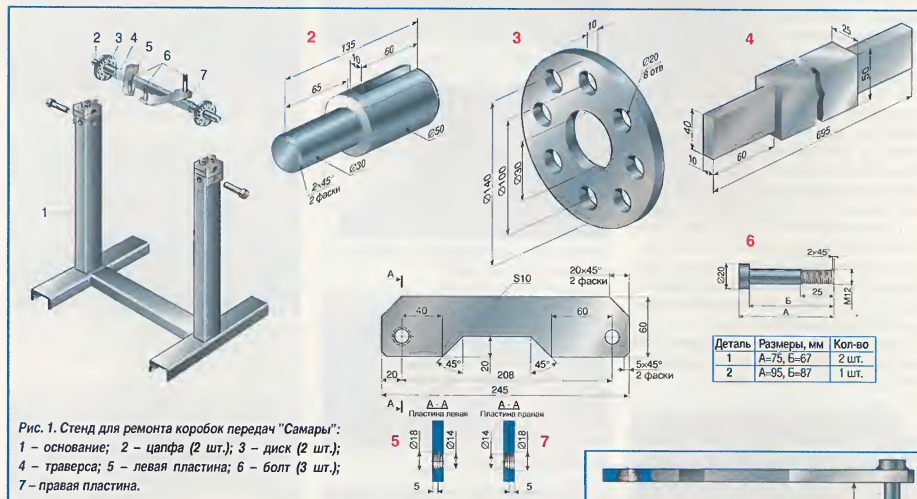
Стенд для ремонта коробок передач "Самары": 1 – основание; 2 – цапфа (2 шт.); 3 – диск (2 шт.); 4 – траверса; 5 – левая пластина; 6 – болт (3 шт.); 7 – правая пластина.
